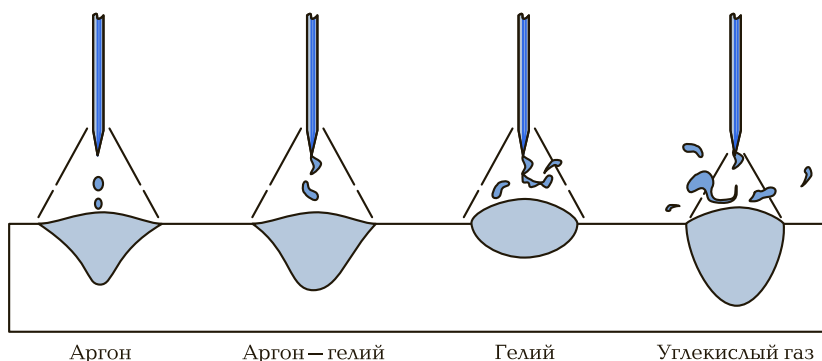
Форма сварного шва и глубина проплавления при сварке в среде различных защитных газов
